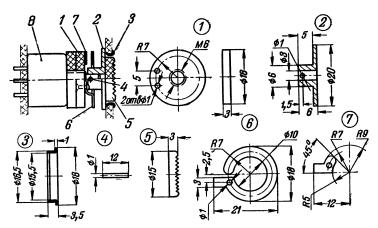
Конструкция выключателя питания и размеры его деталей.
